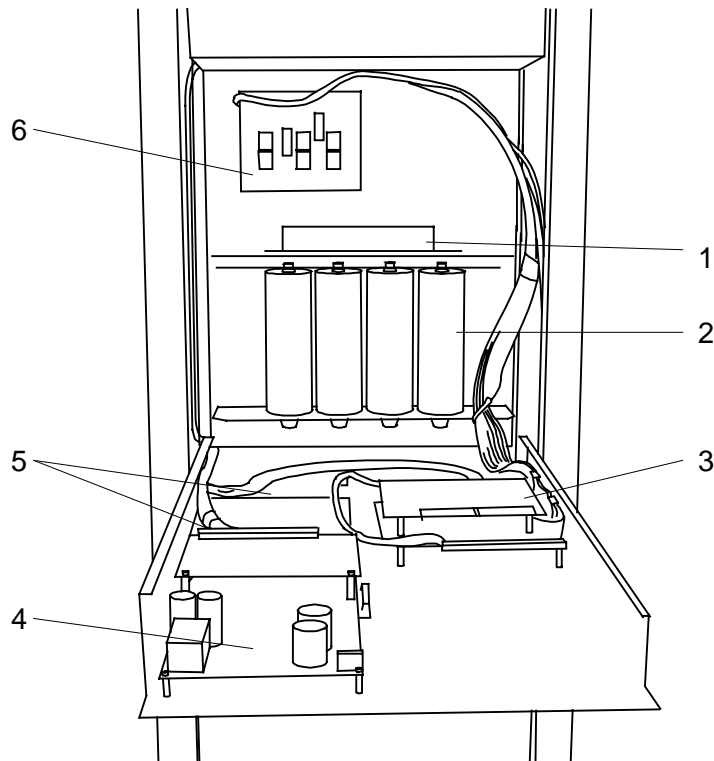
Leiterkarten im Steuergeräteschwenkblech
